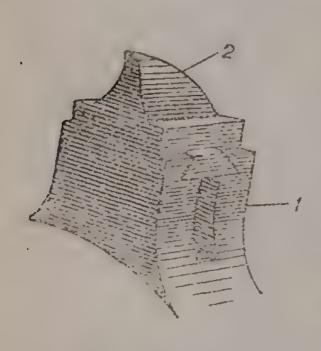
Мушка: 1 — прилив; 2 — мушка
